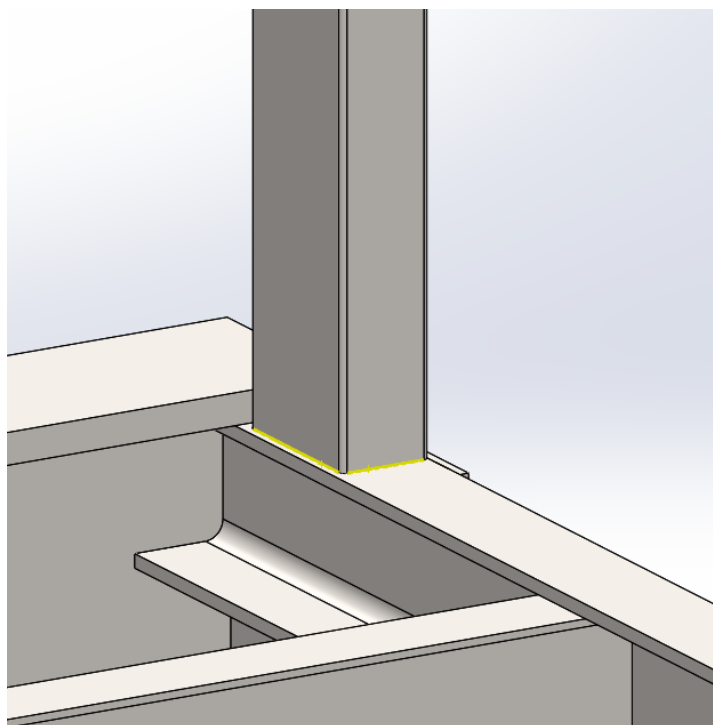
Detalle de cordón de soldadura en pilar trasero
